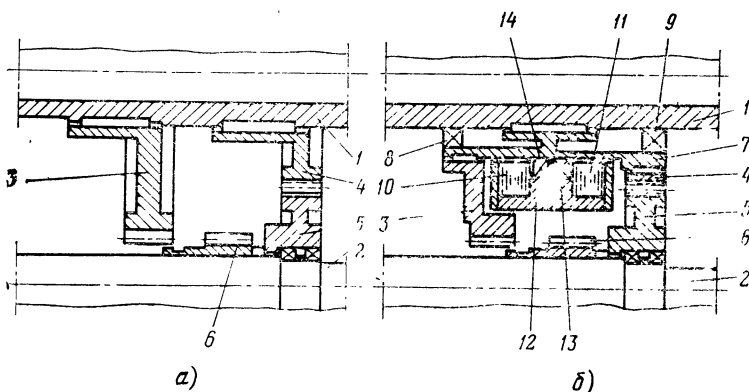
Часть кинематической цепи шпинделя токарного станка 1Б732ФЗ:
